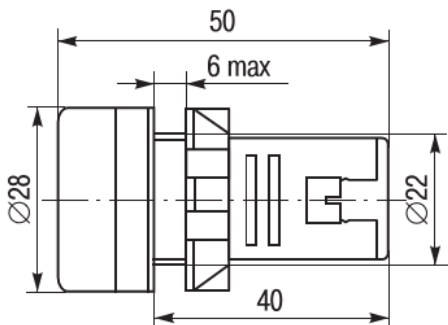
Габаритные, установочные и присоединительные размеры индикатора
